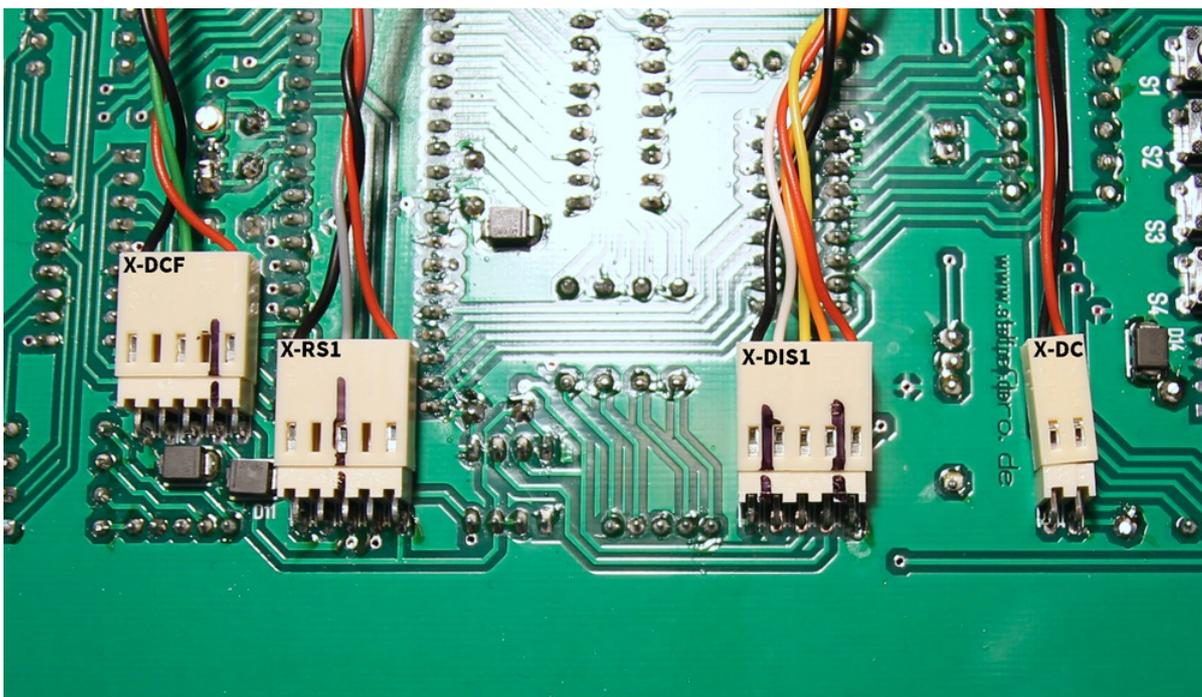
Stecker Beschreibung zum Modul PCB2399
